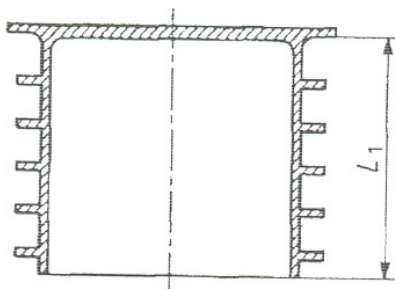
Заглушка типа В для сварки встык
